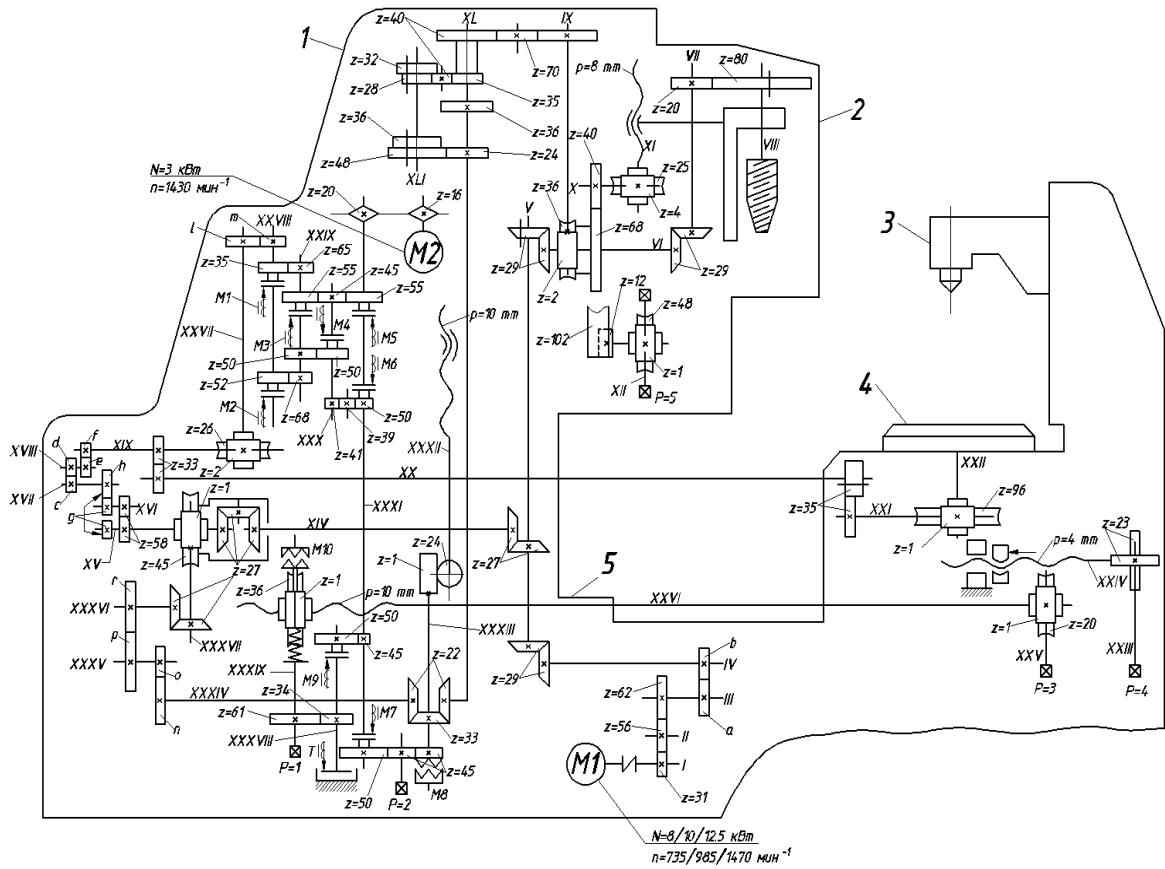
Кинематическая схема зубофрезерного полуавтомата мод. 5К301
